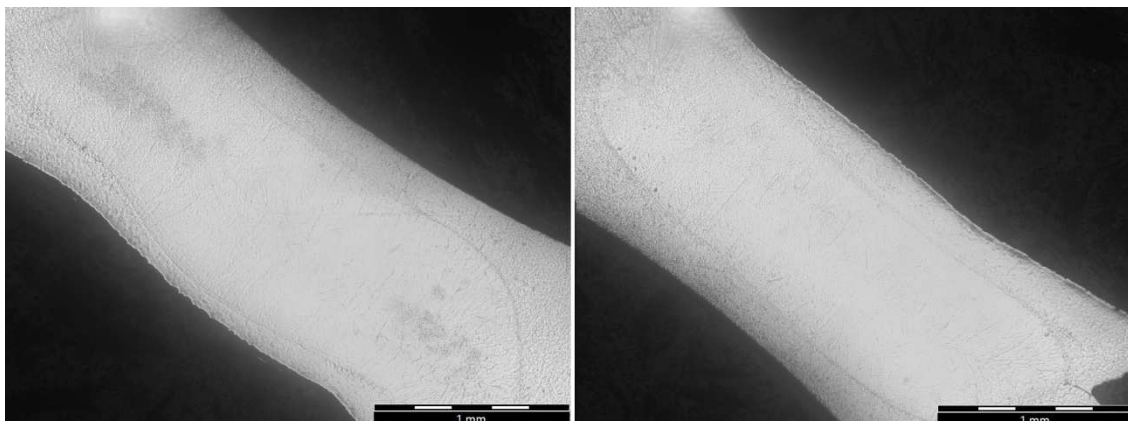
Macrografia das duas lentes de solda do corpo de Prova RCMA36.
